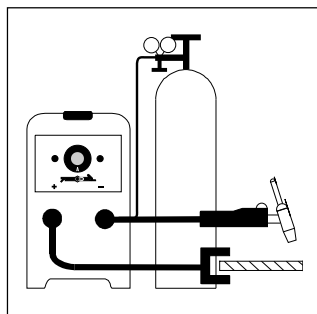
TP 1400 équipé pour le soudage TIG
